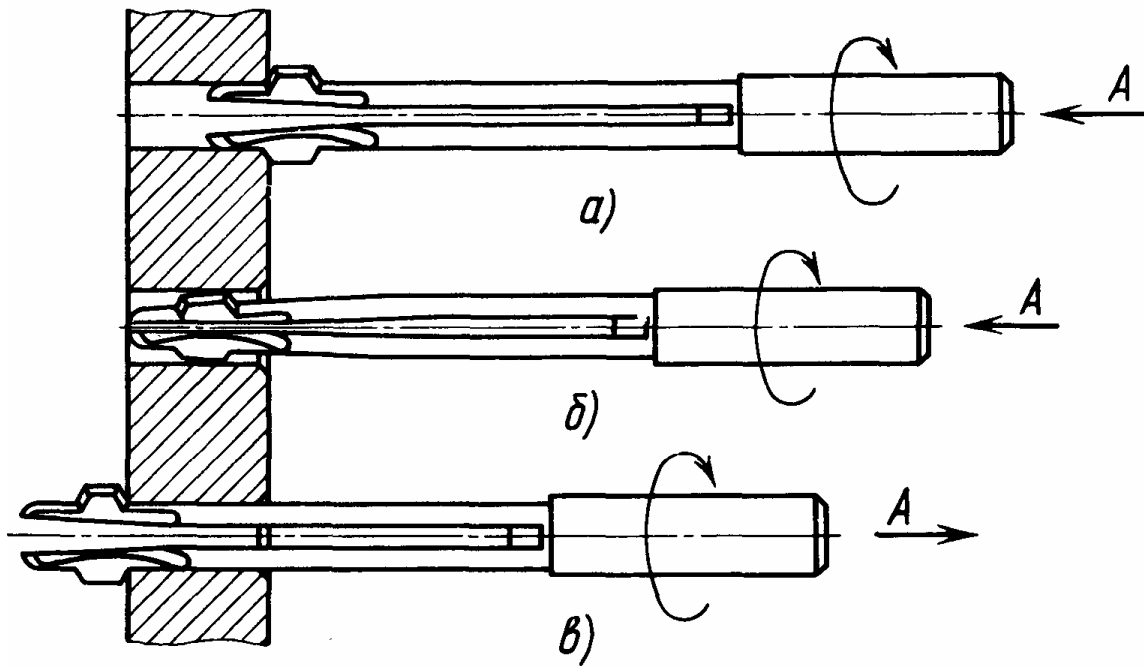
Схеми роботи пружинної зенківки: а – зняття фаски із зовнішнього торця заготовки; б – проміжне положення зенківки; в – зняття фаски з внутрішнього торця; А – напрямок подачі
